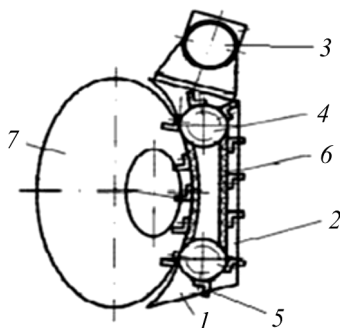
Пример отвала с дисковыми ножами и лентой: 1 – отвал; 2 – несущая рама; 3 – гидромотор; 4 – поворотные барабаны; 5 – скребки; 6 – гибкая лента; 7 – дисковые ножи
